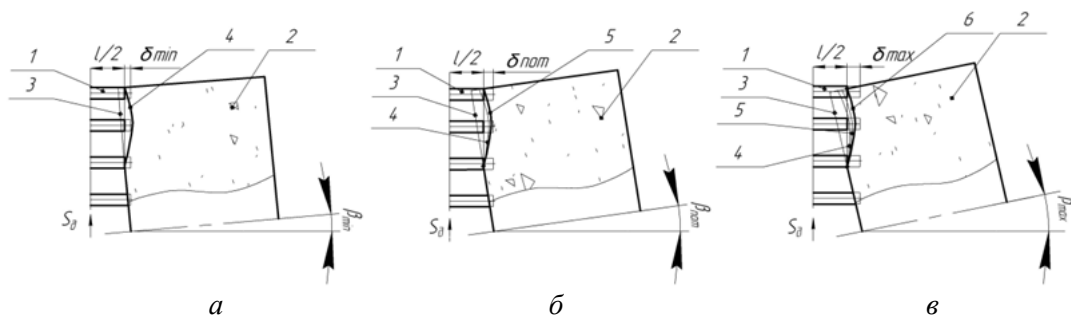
Обробка деталей з різними припусками: 1 – шліфувальний круг; 2 – оброблювана деталь; 3 – профіль шліфувального круга до правки; 4, 5, 6 – профілі калібруючої ділянки шліфувального круга після правки на мінімальну, поточну та максимальну глибину обробки
